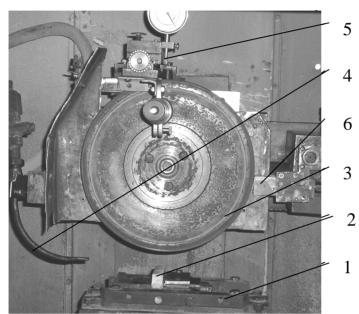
Экспериментальный стенд для комплексного исследования обрабатываемости технической керамики: 1 – динамометрический стол; 2 – образец; 3 –шлифовальный круг; 4 – система для подачи СОТС; 5 – устройство для измерения линейного износа круга; 6 – установка для правки РПК свободным абразивом
